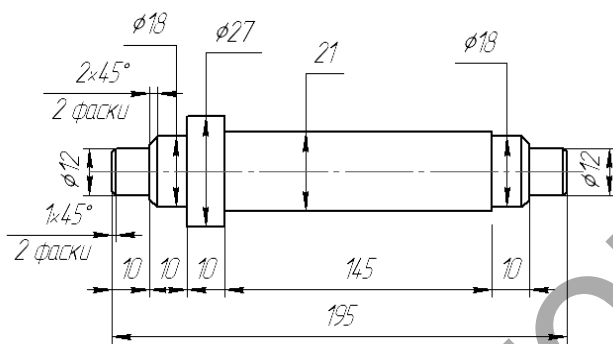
Оправка для выпрессовки и запрессовки гнезда перепускного клапана.
